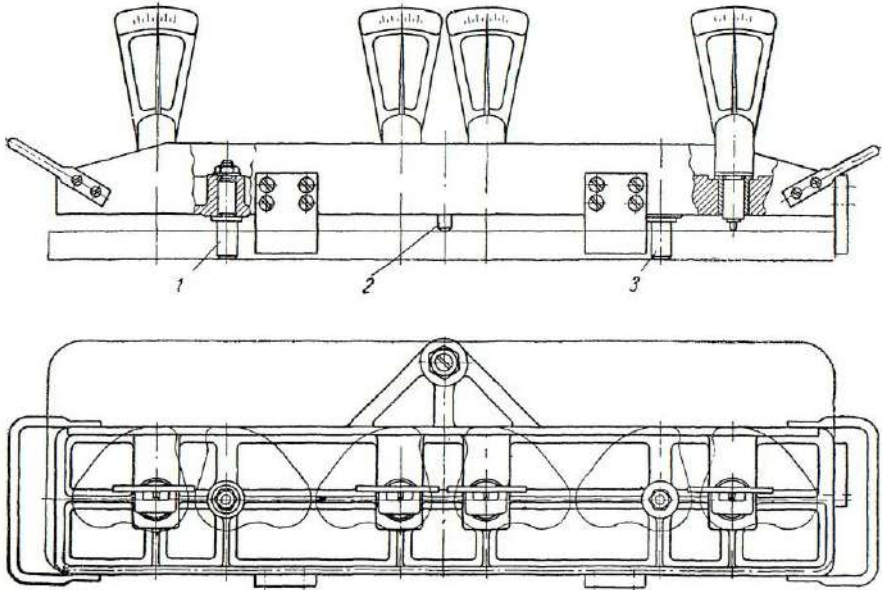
Контрольне пристосування для перевірки заготовки головки блока
